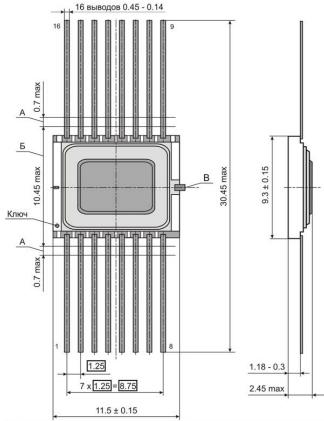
Корпус 402.16-33 размеры в миллиметрах.
